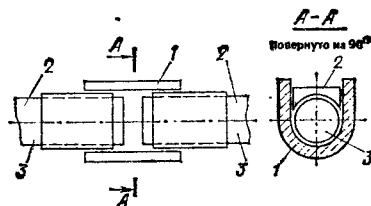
Медная желобчатая подкладка для ванной сварки тесно расположенных стержней
